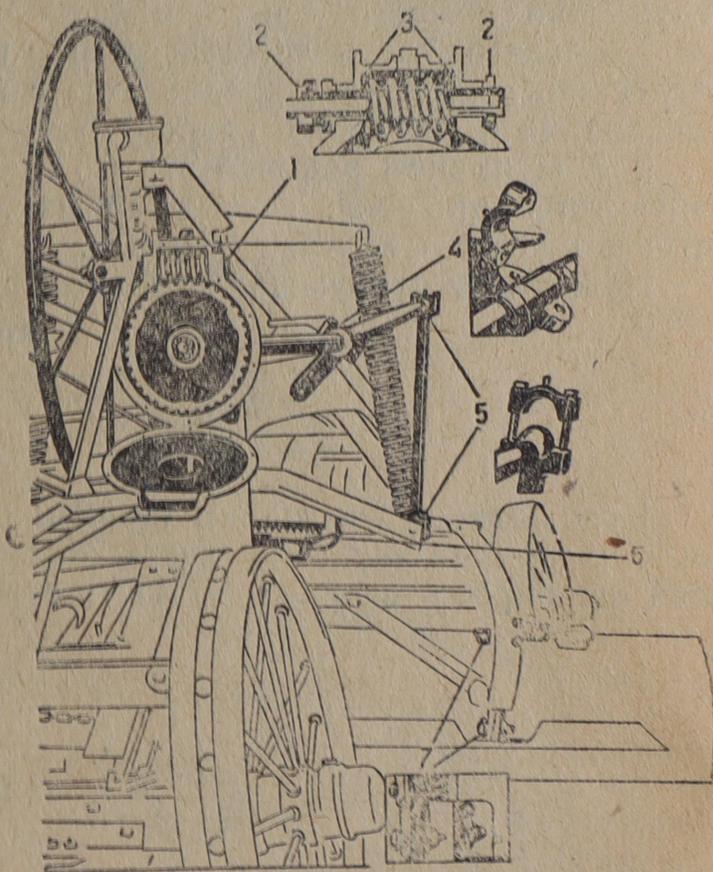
Кривошипно-червячный механизм заглубления ножа.
